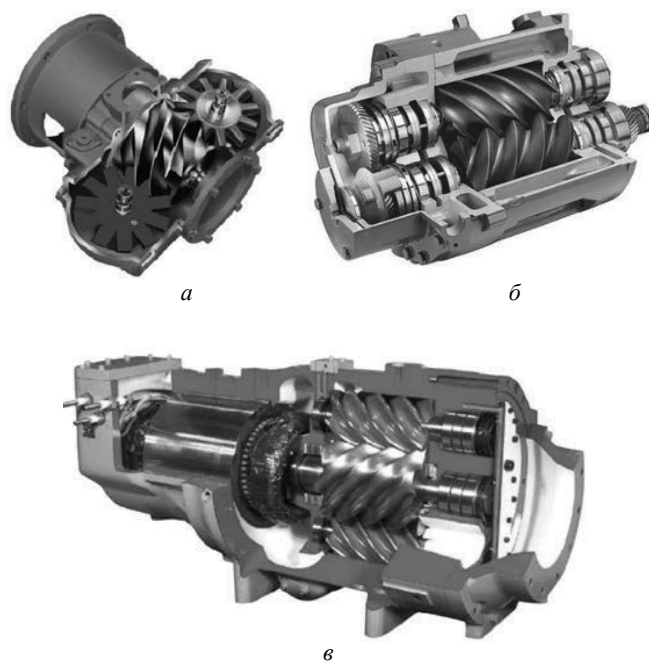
Типы винтовых компрессоров по типу конструкции:
